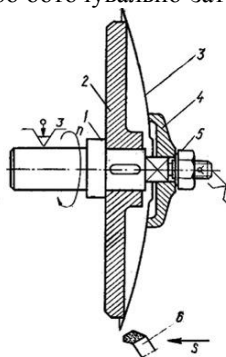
Схема заточування диска на токарно-гвинторізному верстаті: 1 – оправка; 2 – планшайба; 3-диск; 4 – шайба; 5 – гайка; 6 – різець
